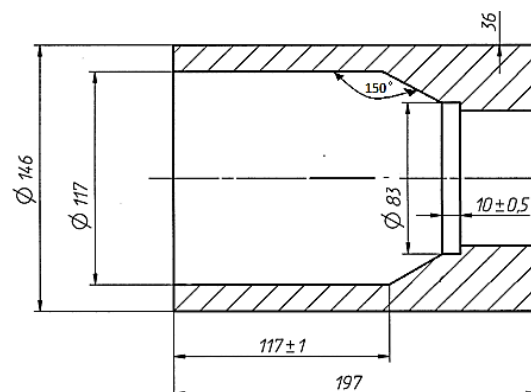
Предлагаемая внутренняя расточка трубы для наплавки «к»
